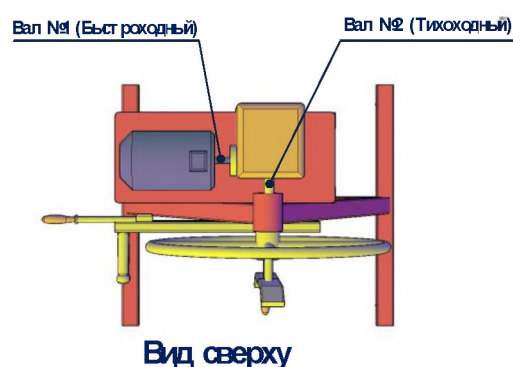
Модернизированный станок ТЦ-11П (вид сверху)
